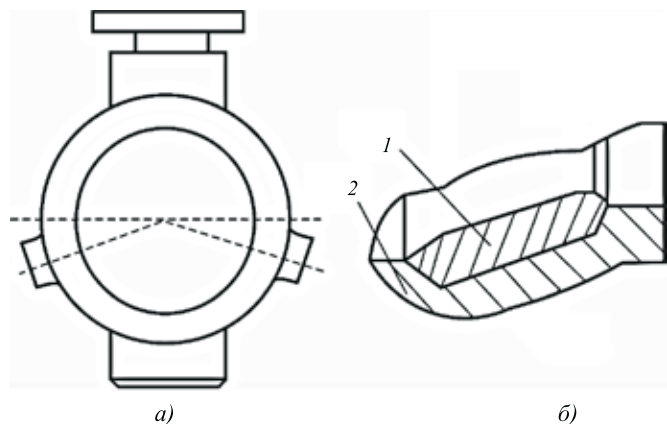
Общий вид поворотного затвора (а) и наплавляемой поверхности (б):
